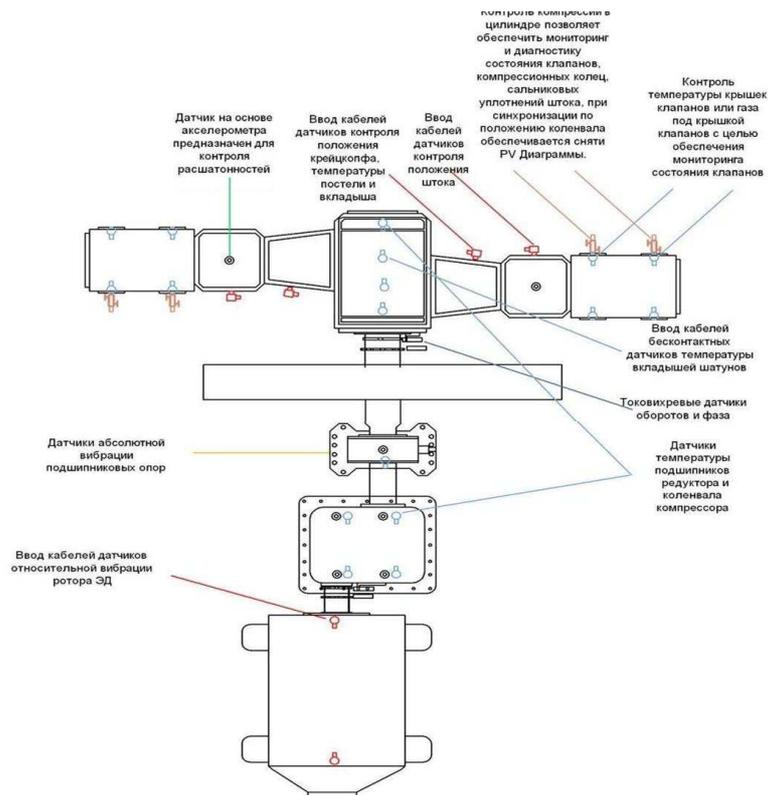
Типовая схема расположения датчиков на агрегате
